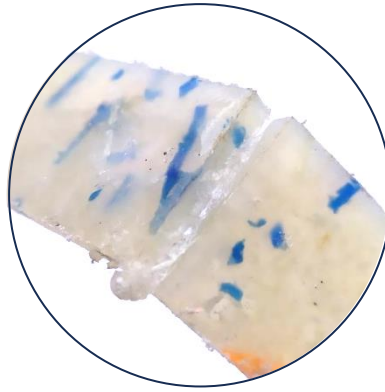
Soldadura 1 lado após pequeno esforço mecânico manual
